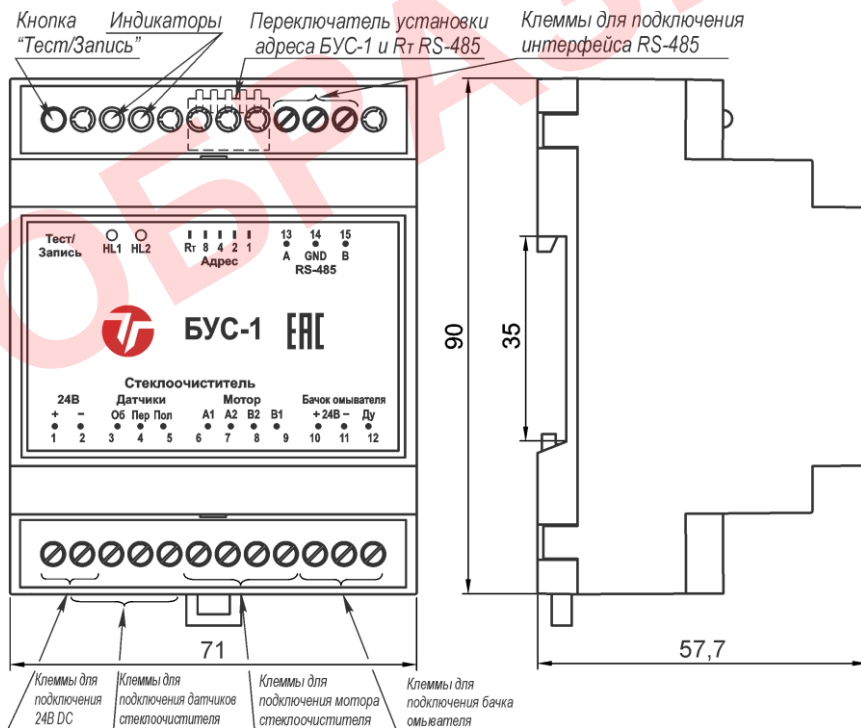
Внешний вид и габаритные размеры БУС-1
